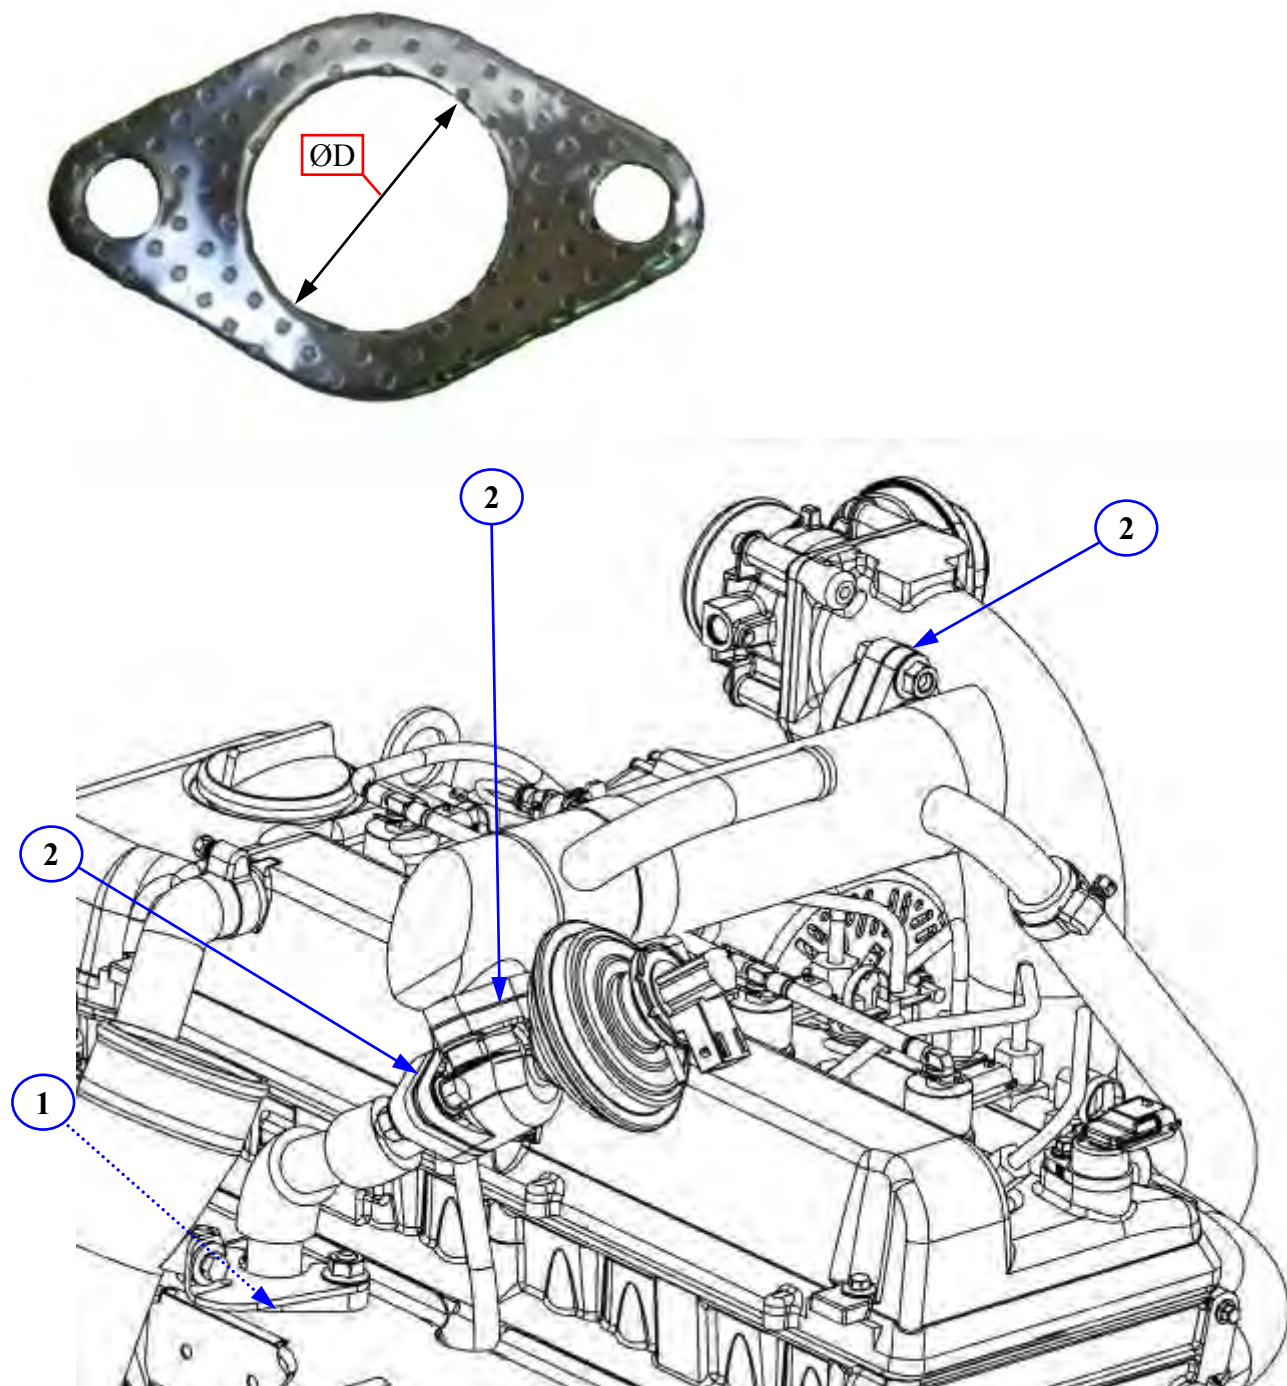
Внешний вид и расположение прокладок клапана рециркуляции.
